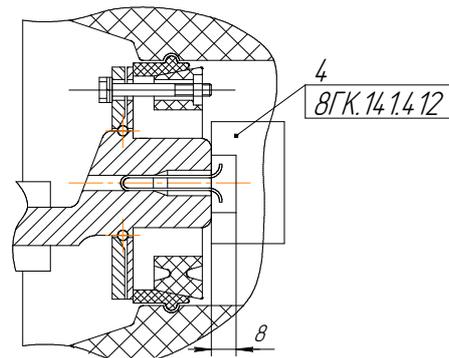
Схема монтажа наружных кронштейнов задних стенок КРУ исполнения УІ на 31,5 кА
